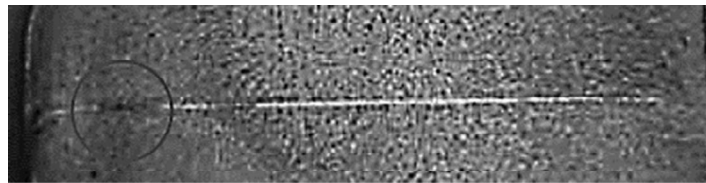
Macrosección de soldadura a tope por destello. Se observa línea blanca que indica zona descarburizada por el efecto de la soldadura. Igualmente encerrado en el círculo oscuro se observa una discontinuidad. (Kim, So, & Kang, 2009)
